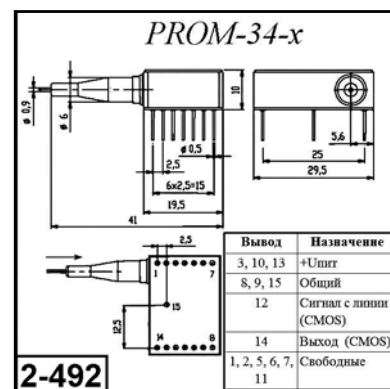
Внешний вид и габаритные размеры модуля PROM-34-x
